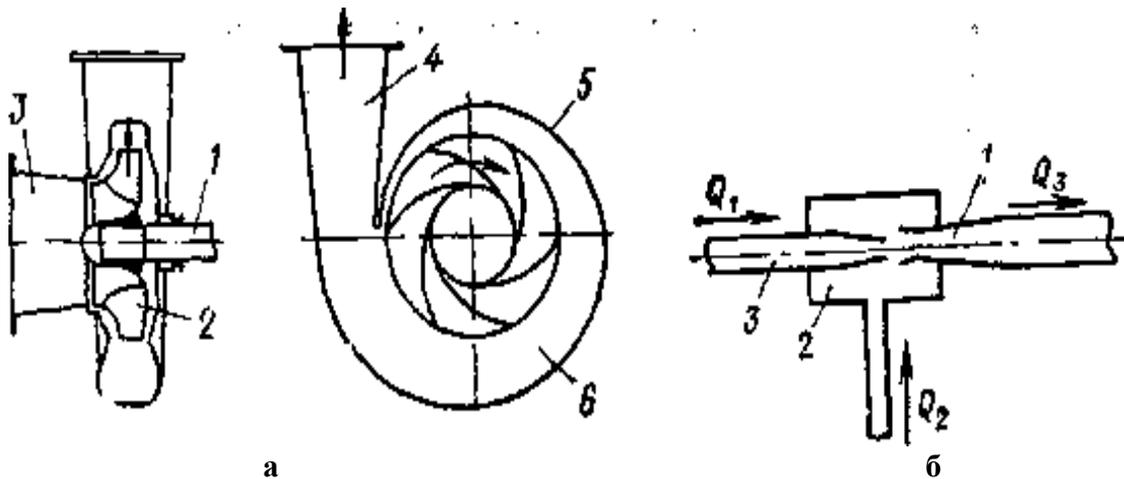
Схемы пожарных насосов: а – центробежного: 1 – вал; 2 – рабочее колесо; 3 – всасывающий патрубок; 4 – напорный патрубок; 5 – корпус; б – спиральная камера; б – струйного: 1 – диффузор; 2 – камера; 3 – насадок
